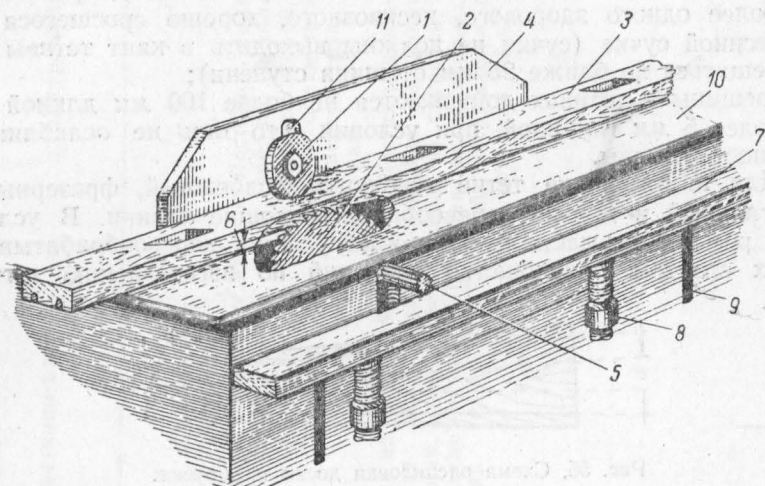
Схема установки круглопильного станка с приспособлением его для фрезеровки гнезд:
